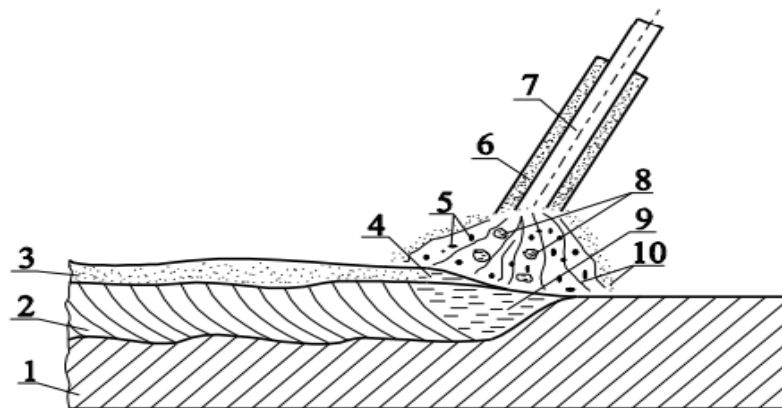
Виникнення зварювальної дуги: 1 – метал, 2 – зварювальний шов, 3 – шлакова корка, 4 – шлакова ванна, 5– частини розплавленої обмазки електрода, 6 – покриті електроди, 7 – стержень електрода, 8 – капля розплавленого стержня електрода, 9 – ванна розплавленого металу, 10 – електрична дуга
